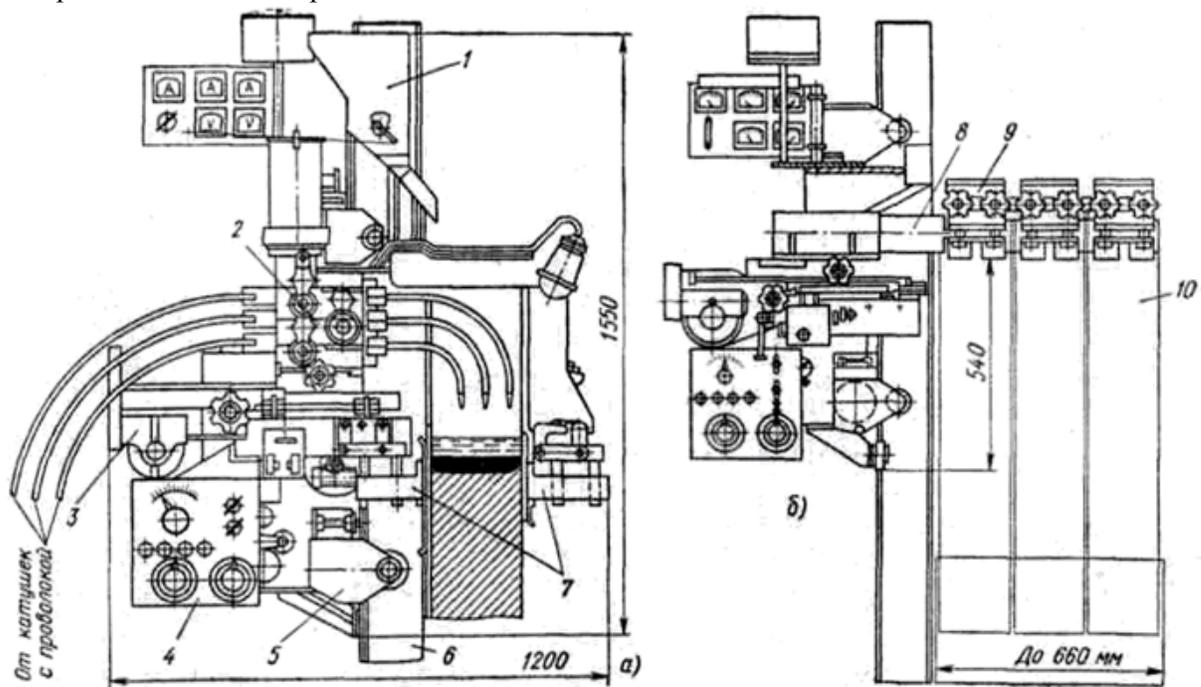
Рельсовый аппарат А-372Р: а — настроенный для сварки электродной проволокой; б — настроенный для сварки пластинчатыми электродами прямолинейных стыков:
